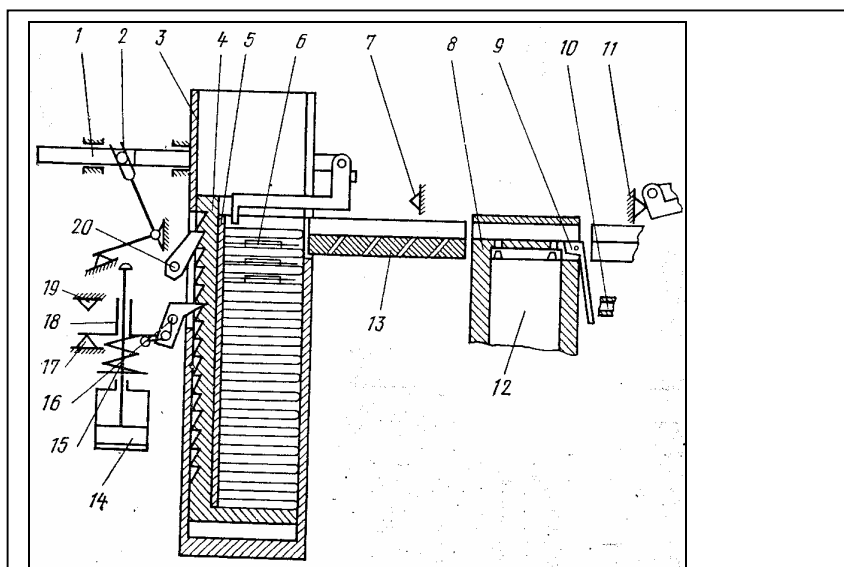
Механизм загрузки-выгрузки корпусов ИС
